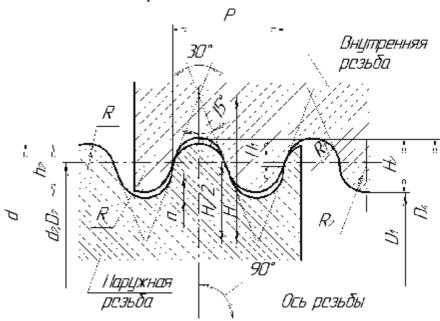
Профиль круглой резьбы по ГОСТ 13536-68
